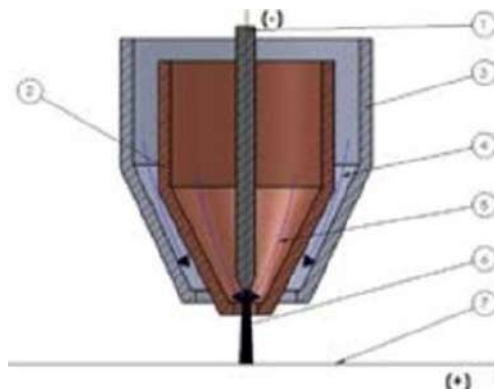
Принципова схема зварювального плазмотрону [39]: 1 – неплавкий електрод; 2 – плазмоутворююче сопло; 3 – захисне сопло; 4 – захисний газ; 5 – плазмоутворюючий газ; 6 – плазмова дуга; 7 – виріб.
